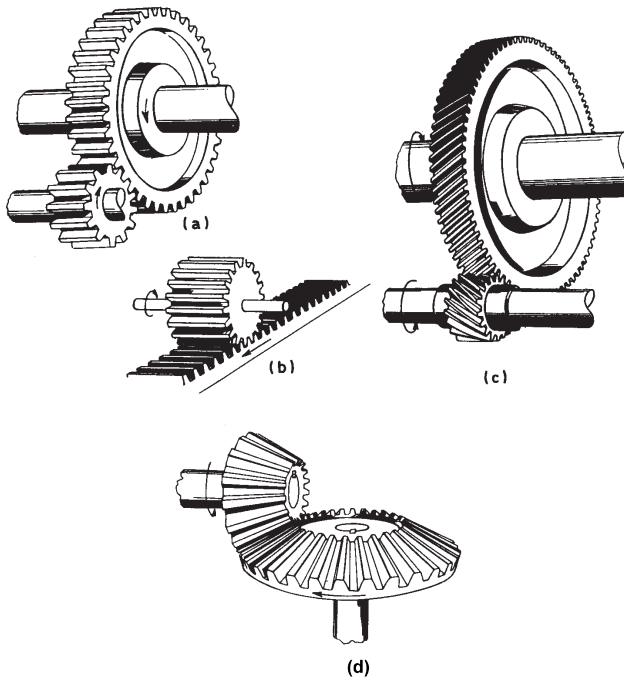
Mecanismos elementales. Engranajes: (a) engranajes cilíndricos de dientes rectos, (b) cremallera, (c) engranajes cilíndricos con dientes helicoidales, (d) engranajes cónicos
